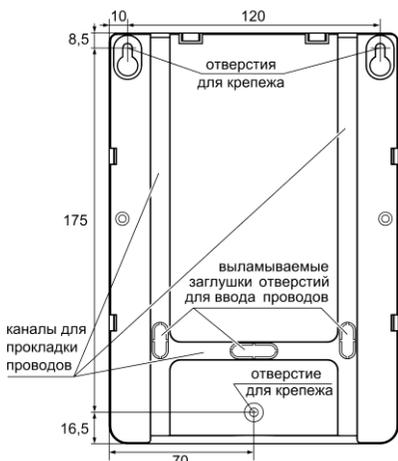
Задняя стенка АС. Расположение отверстий для крепежа. Присоединительные размеры
